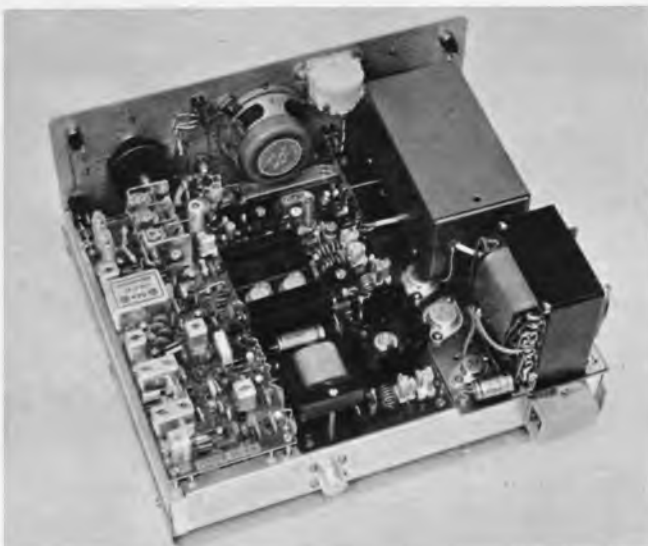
Innenansicht des fertigen Funksprechgerätes, Blick auf das Chassis
